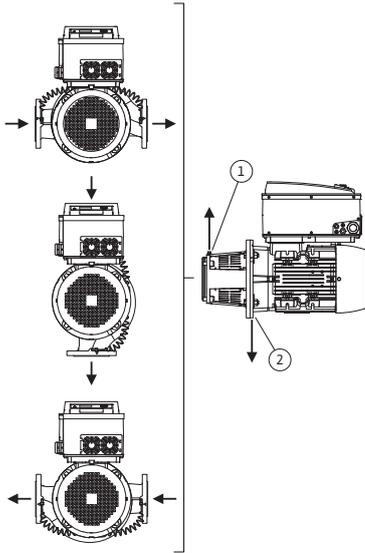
Positions de montage autorisées avec arbre moteur horizontal
